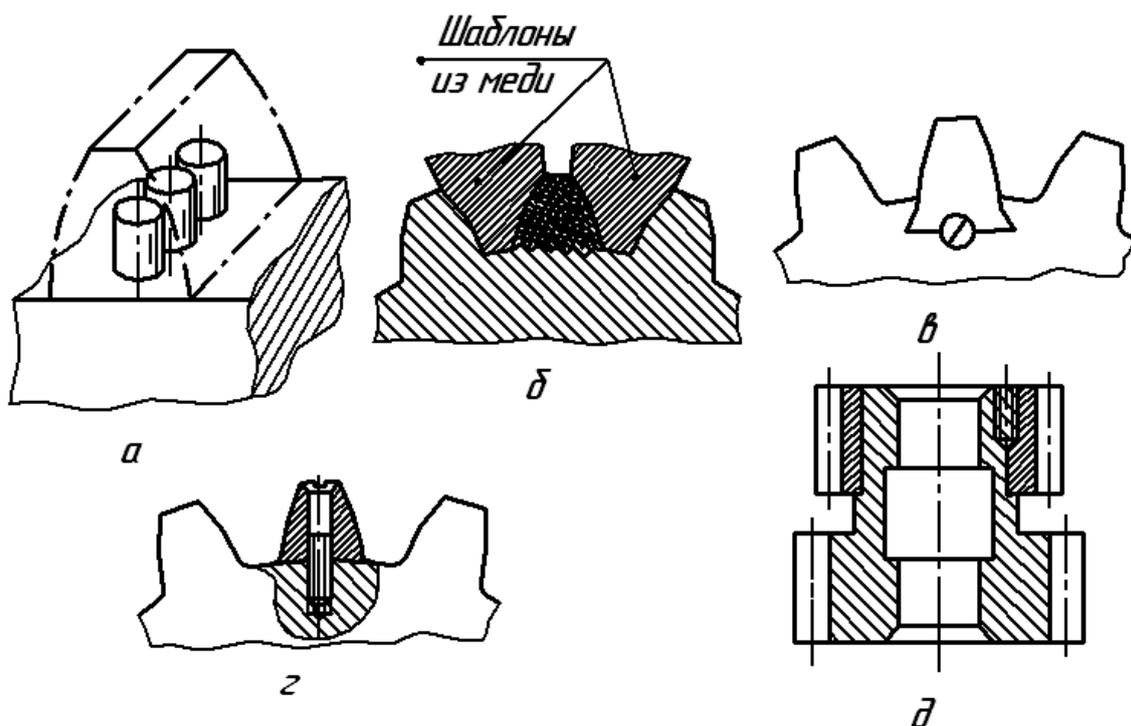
Методы ремонта зубьев зубчатых колес.
